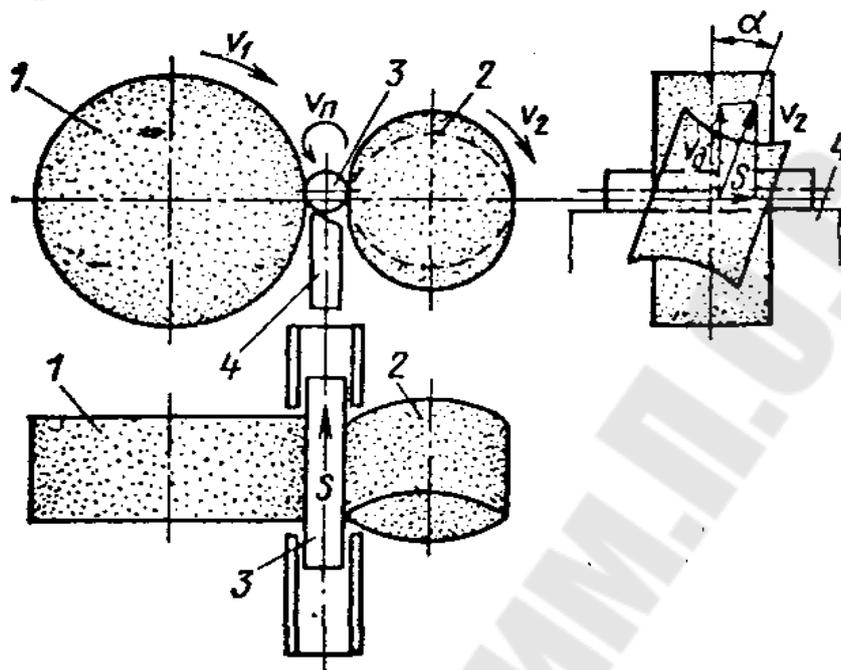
Схема шлифования на бесцентрово-шлифовальном станке
